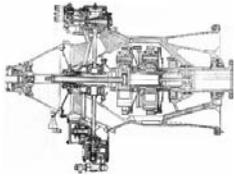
Продольный разрез редуктора с коробкой приводов агрегатов
